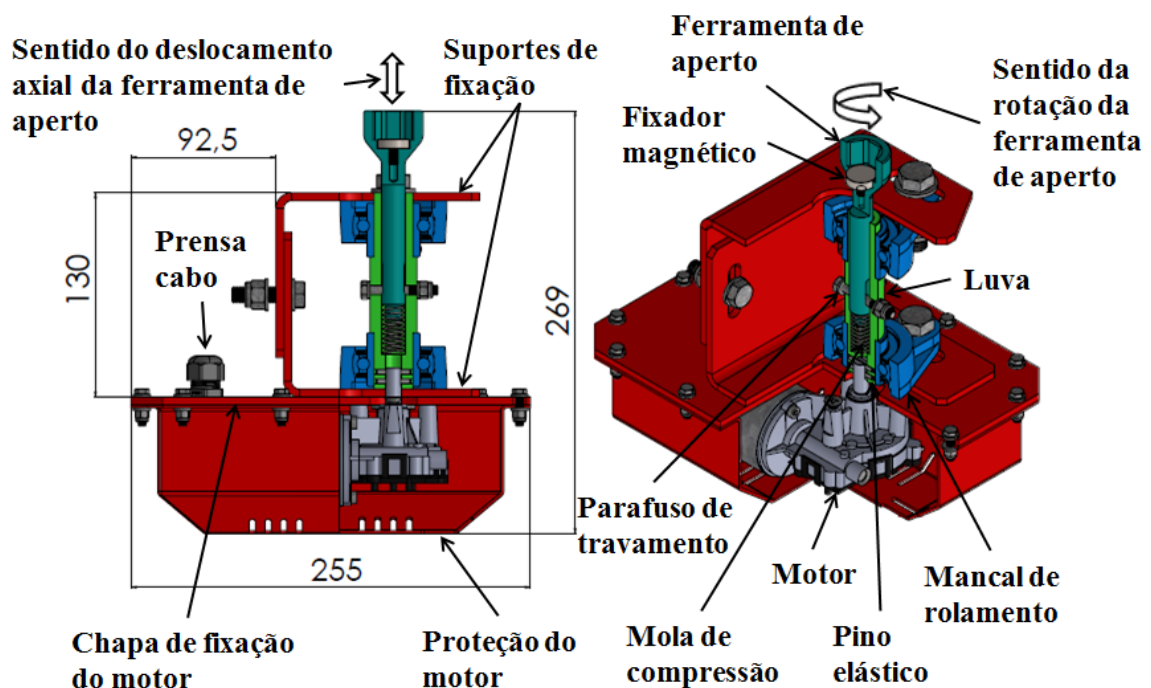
Vista em corte do suporte posicionador do *clamp* com fixador magnético
